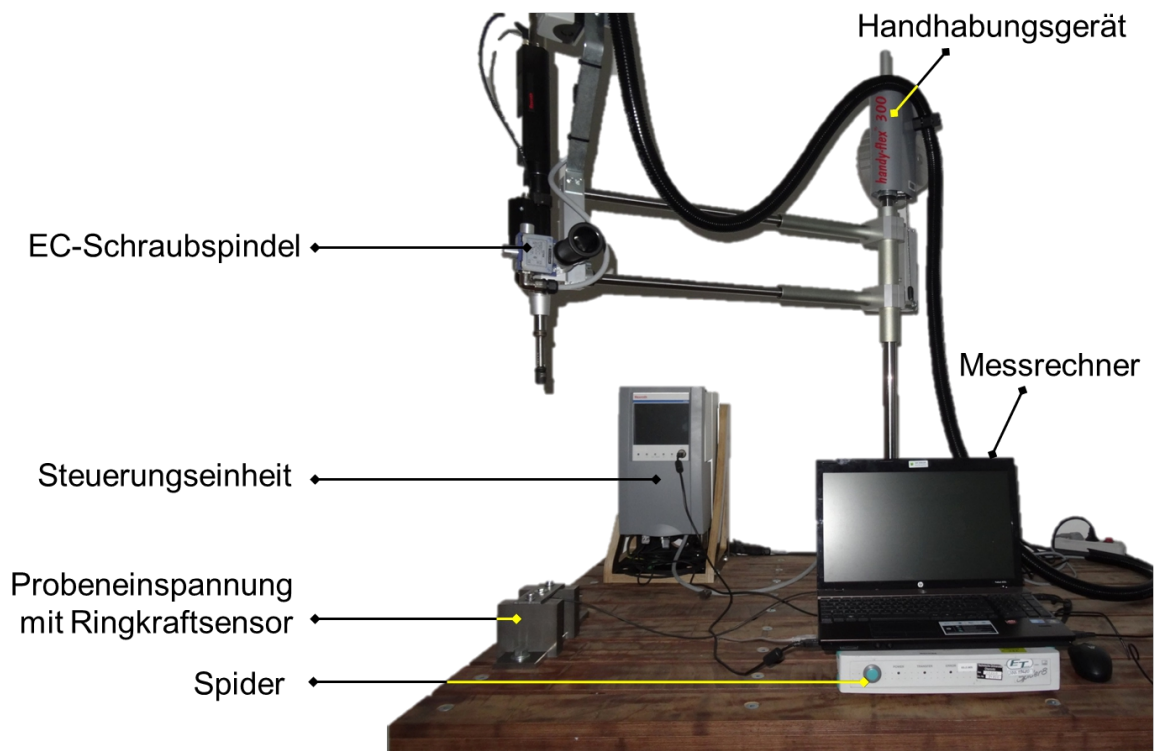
Verschraubungsprüfstand, EC-Schraubspindel Fa. Bosch Rexroth
